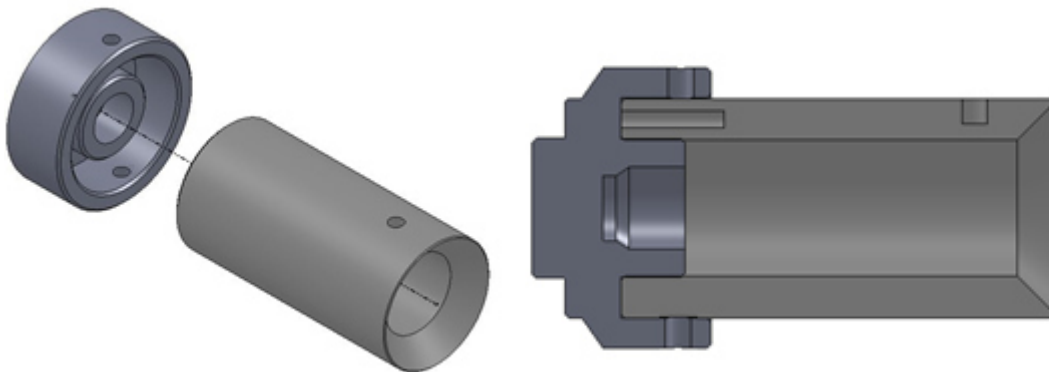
Nuevo acople del cilindro de extrusión a su base, 3D CAD Design Software SolidWorks
